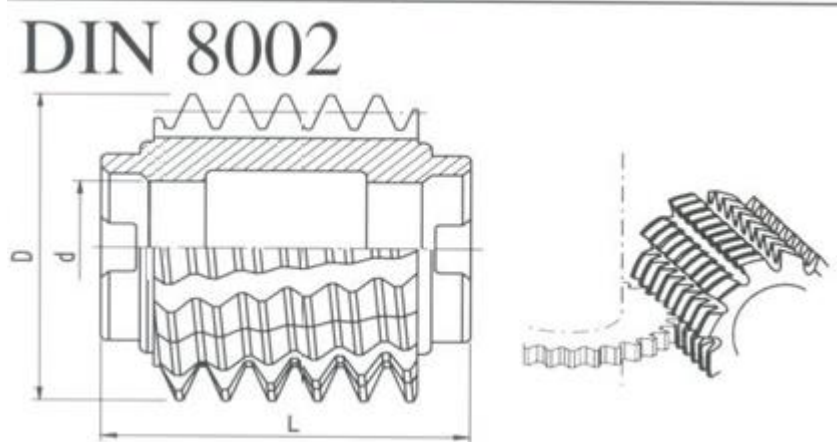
Фреза DIN 8002 9431 5 [9, с. 13]
